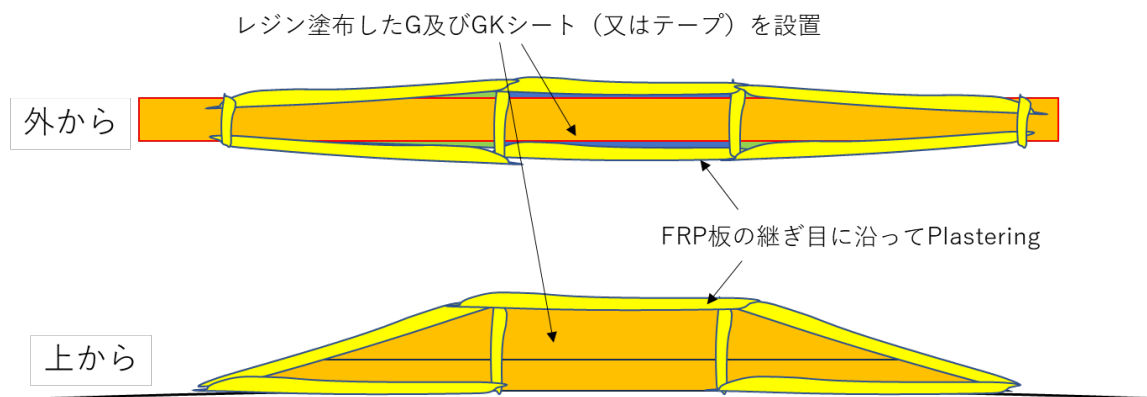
パンケーキジョイント（箱型）への絶縁施工例
